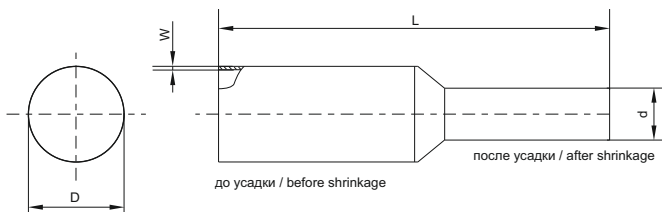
Габаритные размеры ТПУ / Figure 1 – Overall dimensions of TPU
